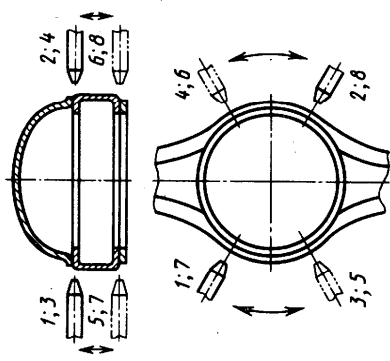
Последовательность постановки прихваток после сборки корпуса с крышкой и фланцем
